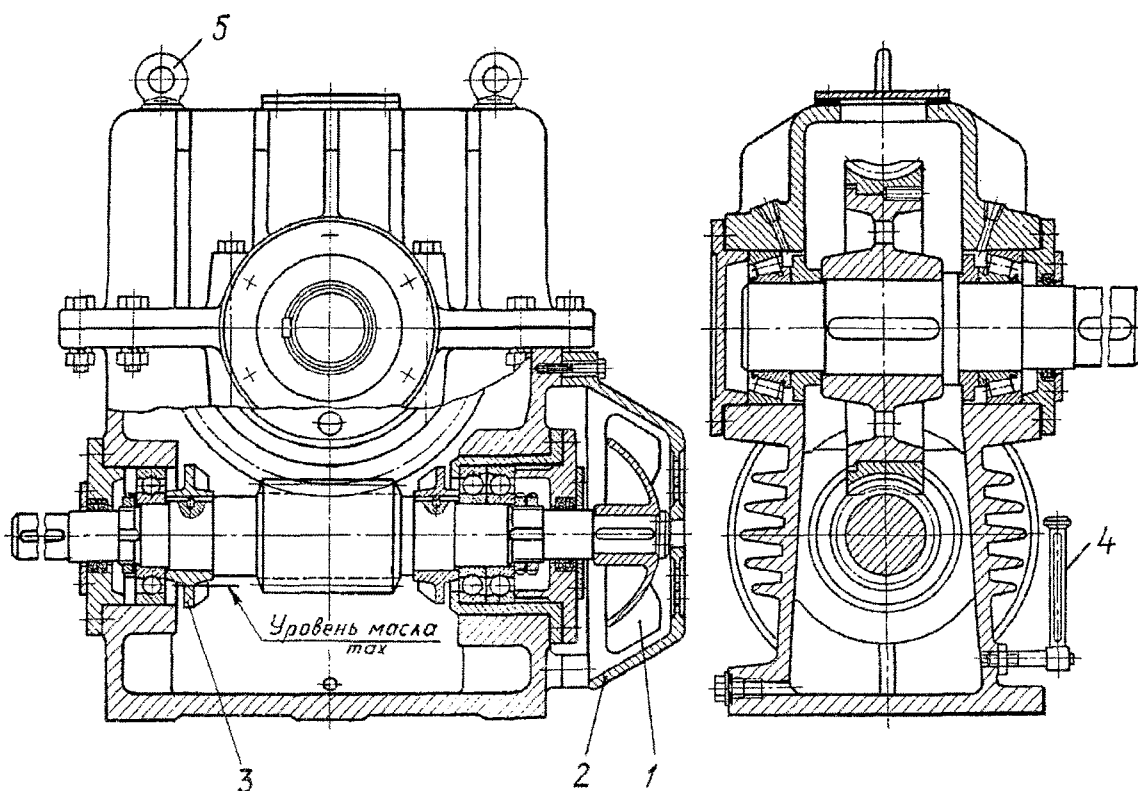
Одноступенчатый червячный редуктор с искусственным охлаждением
